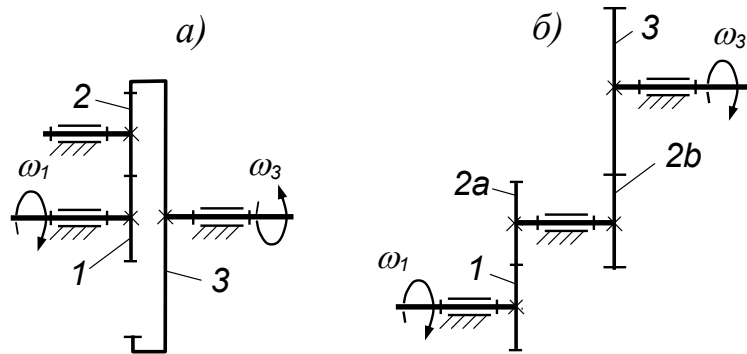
Цилиндрические зубчатые передачи с неподвижными осями:
